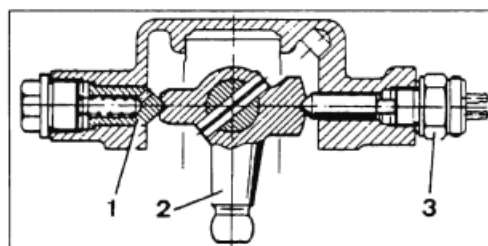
Частковий розріз картера привода перемикання передач:
